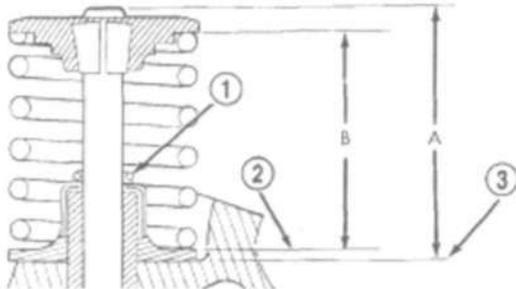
Проверка высоты установки пружины и размера высоты наконечника клапана
